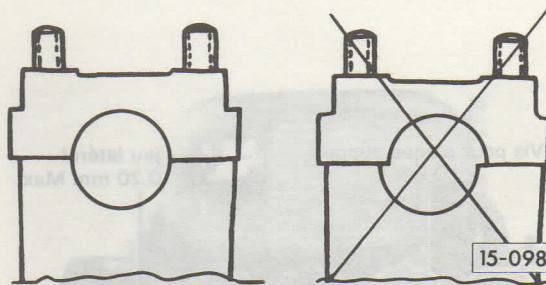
Chapeau de palier d'arbre à cames : position de montage
